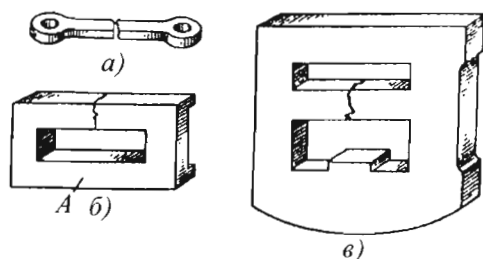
Выбор способа подогрева при ремонтной сварке чугуна:
